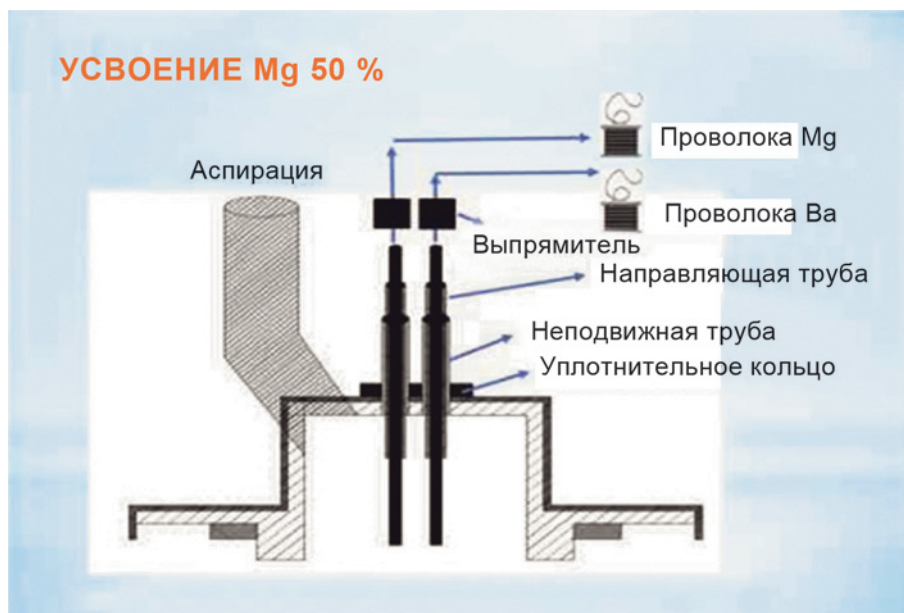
Конструкция крышки ковша, обеспечивающая вертикально направленный ввод проволоки
